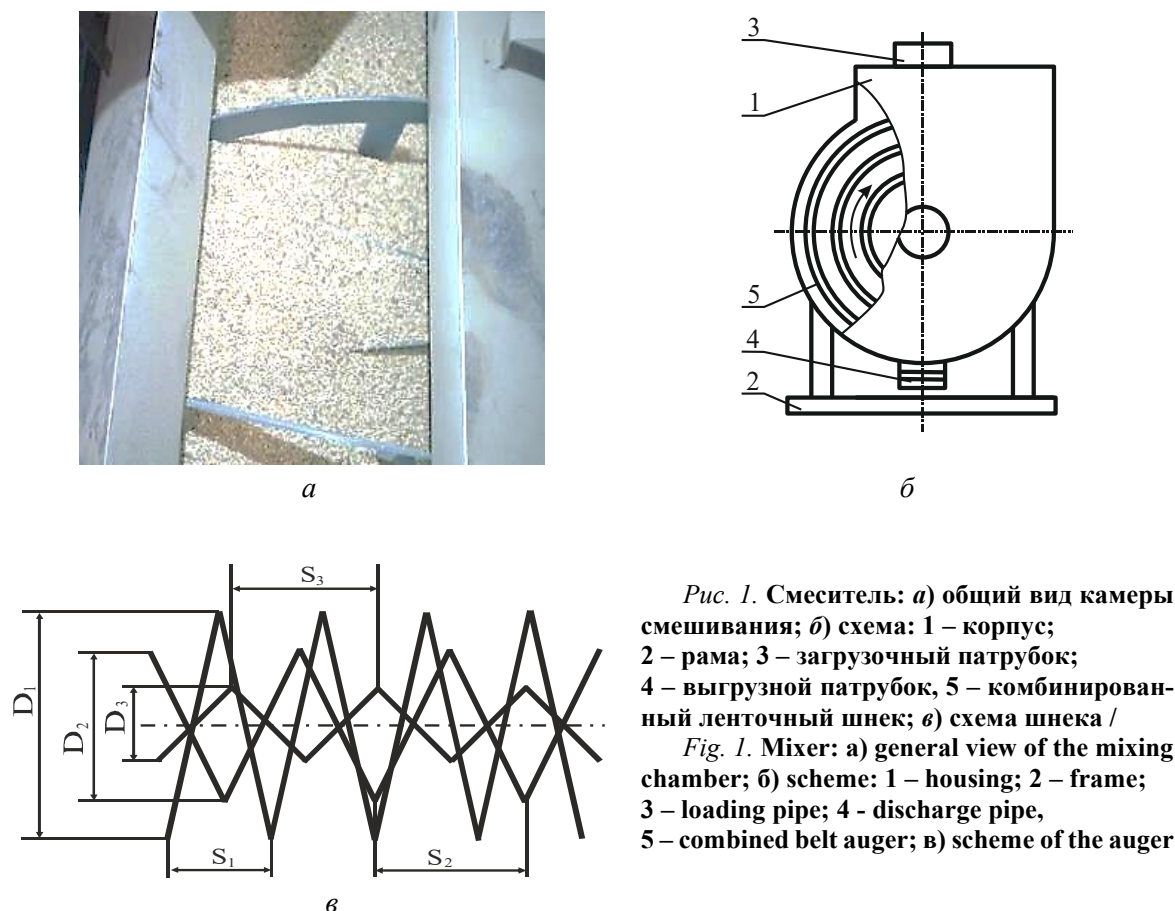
Смеситель: а) общий вид камеры смешивания; б) схема: 1 – корпус; 2 – рама; 3 – загрузочный патрубок; 4 – выгрузный патрубок, 5 – комбинированный ленточный шнек; в) схема шнека /
